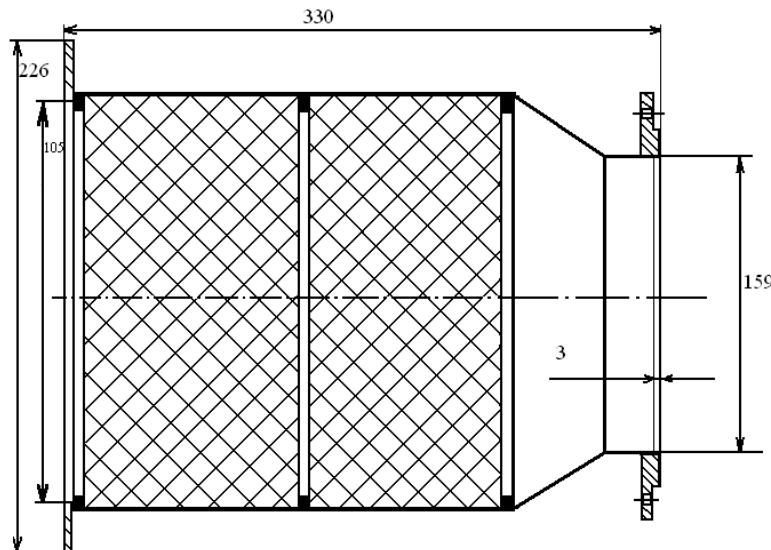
Габариты и схема расположения каталитического нейтрализатора в корпусе для испытания на КамАЗе
